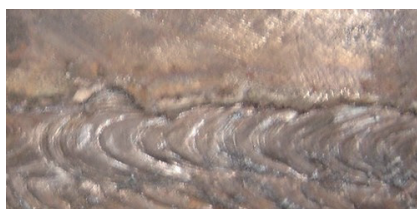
| Defeitos em soldas, avaliadas por inspeção visual
